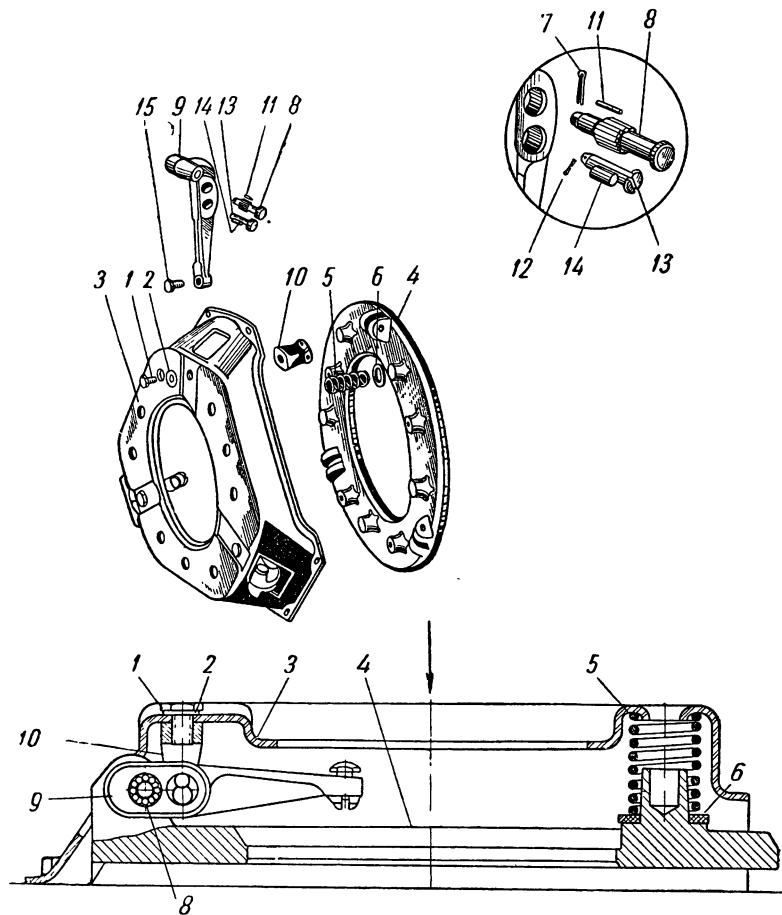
Разборка нажимного диска сцепления с кофухом в сборе
